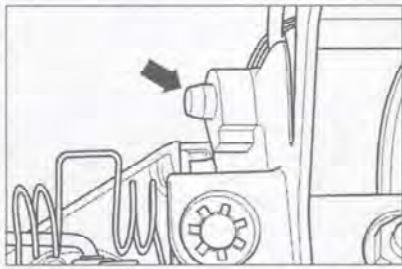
Перед установкой педали сцепления отрегулируйте шкворень шарнира педали таким образом, чтобы он слегка выступал из опорного кронштейна (стрелка).
